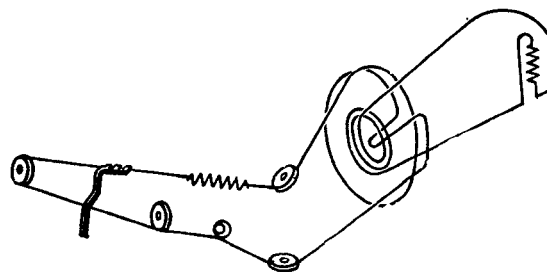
Кинематическая схема верньерного устройства радиолы «Рекорд-354»
